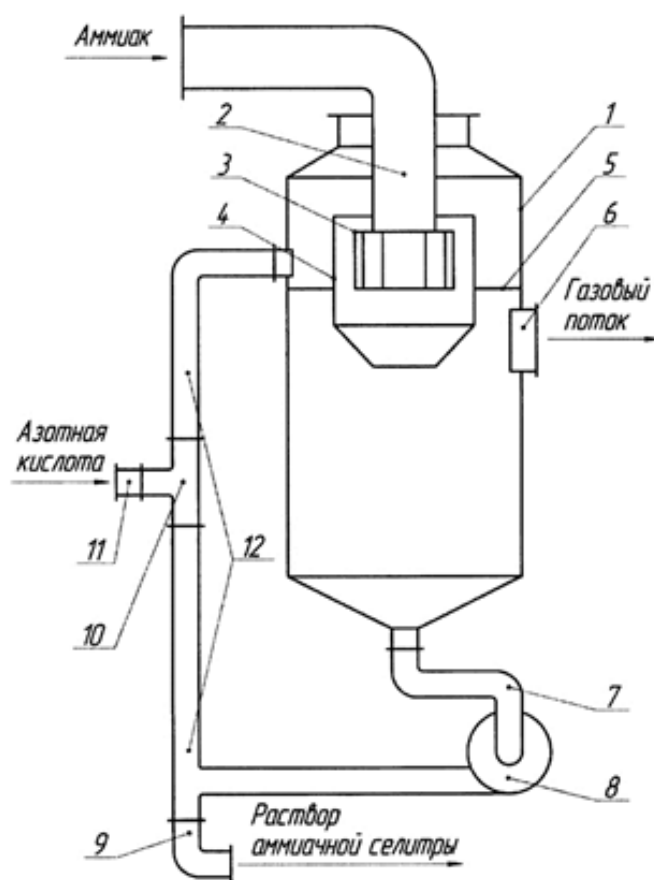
Вихревой абсорбер аммиака: 1-корпус; 2-патрубок подачи газообразного аммиака; 3-стакан; 4-обечайка; 5-тарелка; 6-патрубок вывода газового потока; 7-всасывающий трубопровод; 8-насос; 9-патрубок вывода раствора аммиачной селитры; 10-смеситель азотной кислоты; 11-патрубок подачи азотной кислоты (соединен со смесителем); 12-нагнетательный трубопровод
